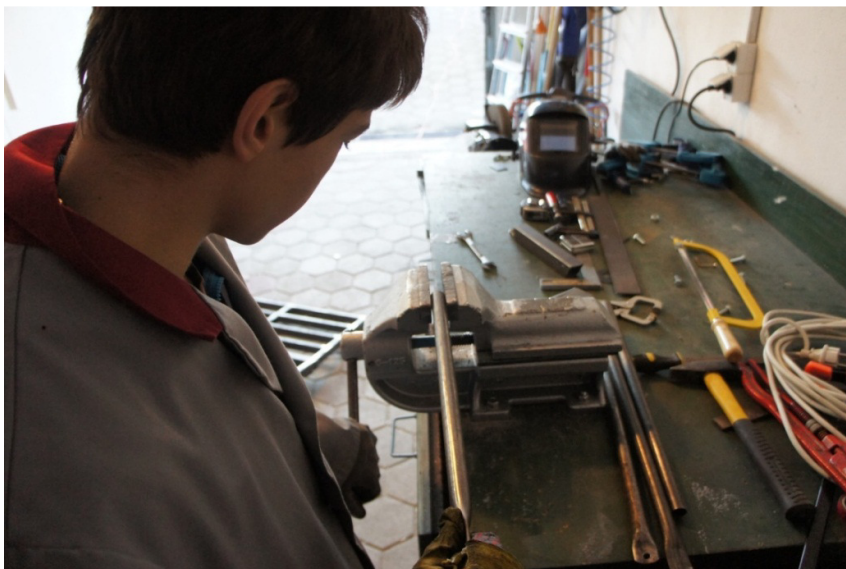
Piljenje vodilnega profila (foto: Jože Hrovat).
